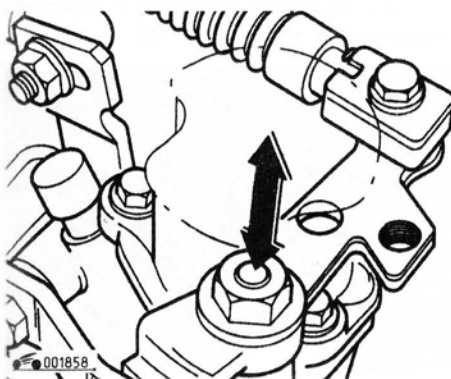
Проверка вертикального перемещения вала механизма выбора передач
